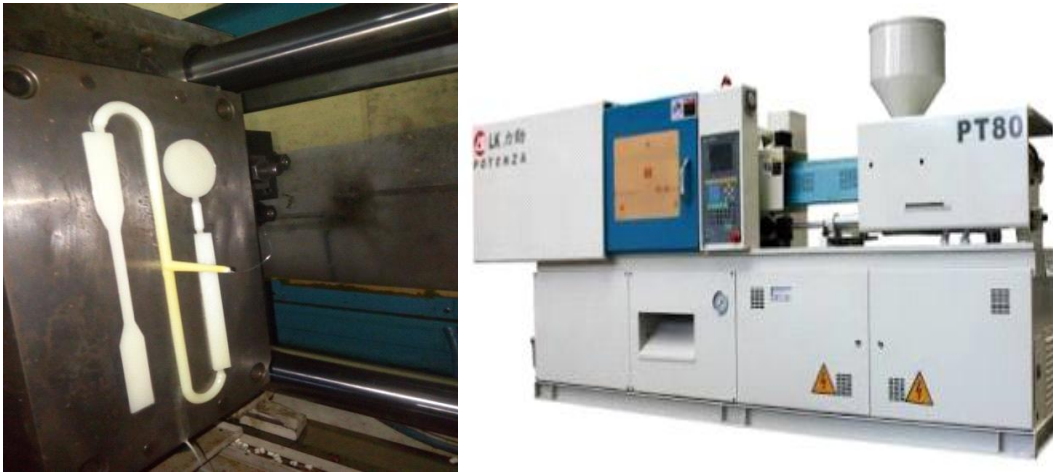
l'élaboration des éprouvettes à partir d'une presse à injection
